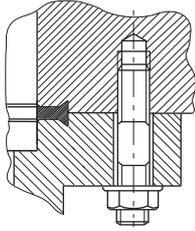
Flanschverbindung CF-F, Stiftschraube und Gewindebohrung
